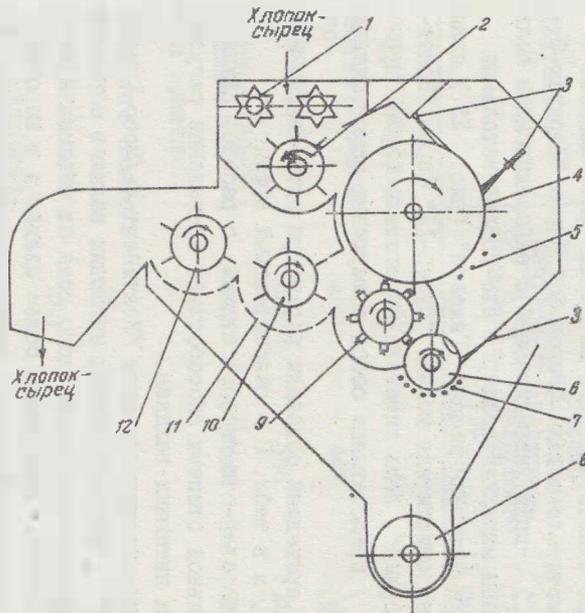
Питатель-очиститель модели "Regal-88" фирмы "Хард-Эттер": 1 - питающие валики; 2 - питающий колковый барабан; 3 - протирачные щетки; 4 - пильный барабан; 5 - колосники; 6 - регенерационный пильный барабан; 7 - колосниковая решетка; 8 - соровыводящий пнек; 9 - съемный барабан; 10 - колковый барабан; 11 - сетка; 12 - колковый барабан
